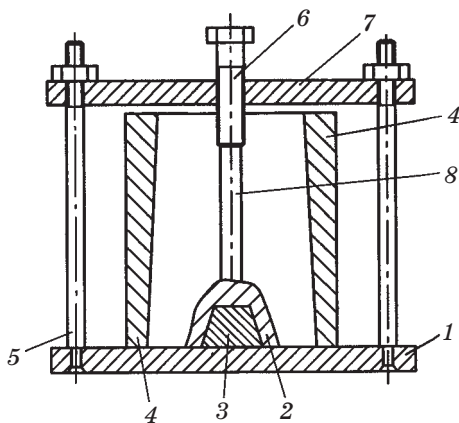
Оснастка для заливки гальванопластического осадка металлом:
